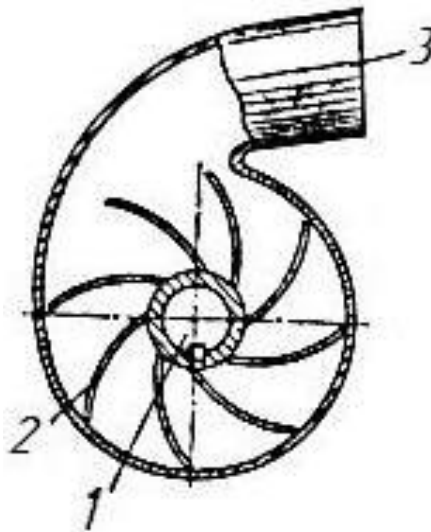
Відцентровий насос: 1 – всмоктувальний рукав; 2 – робоче колесо; 3 – напірний рукав.
